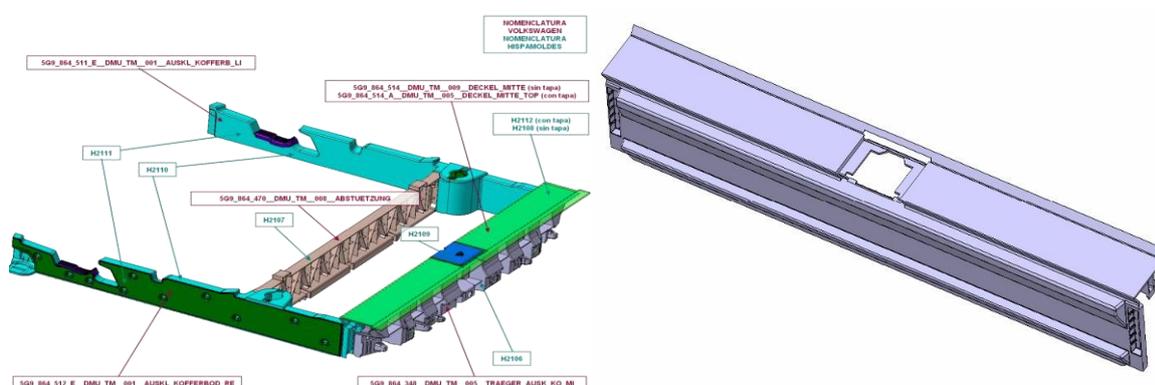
Conjunto completo y detalle de la pieza ejemplo elegida para el Proyecto.
